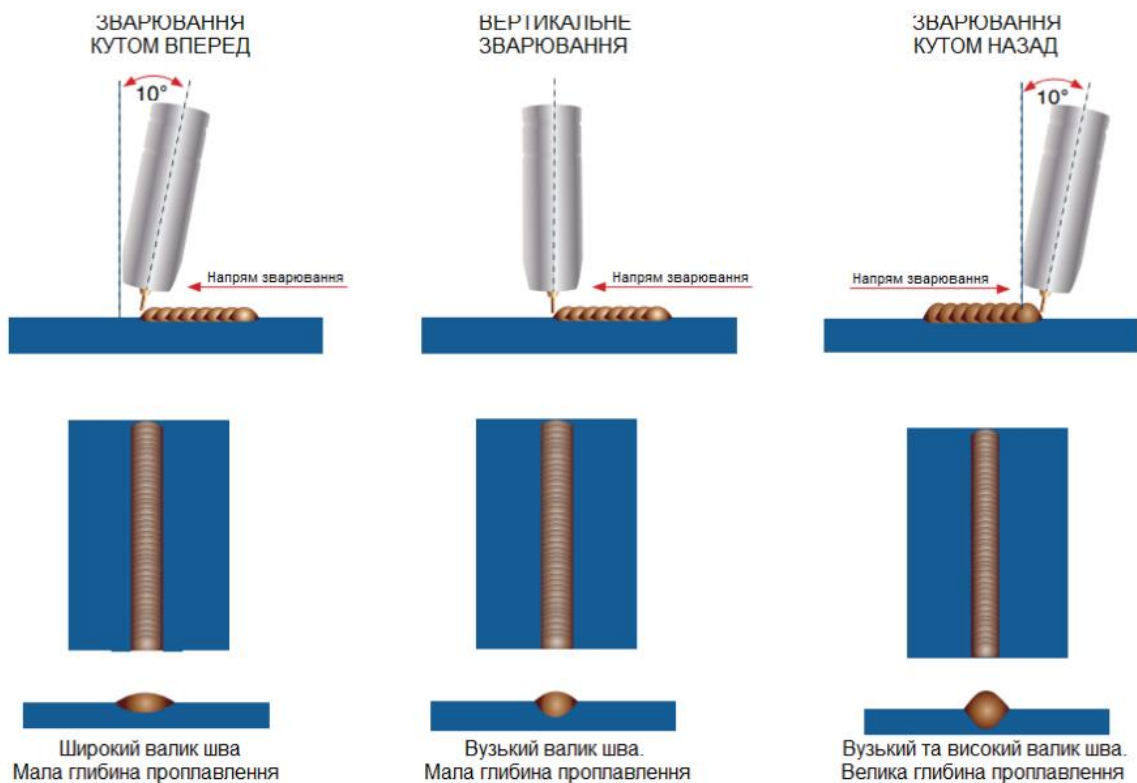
Приклад впливу нахилу зварювального пальника на провар та форму шва
